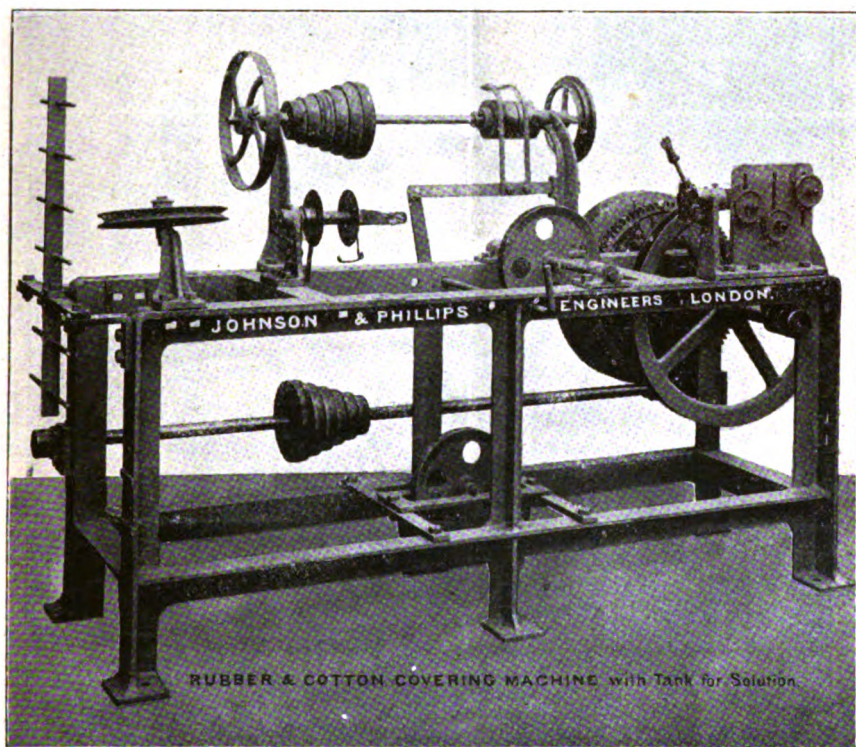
Machine à guipper les fils et à les recouvrir de caoutchouc.
